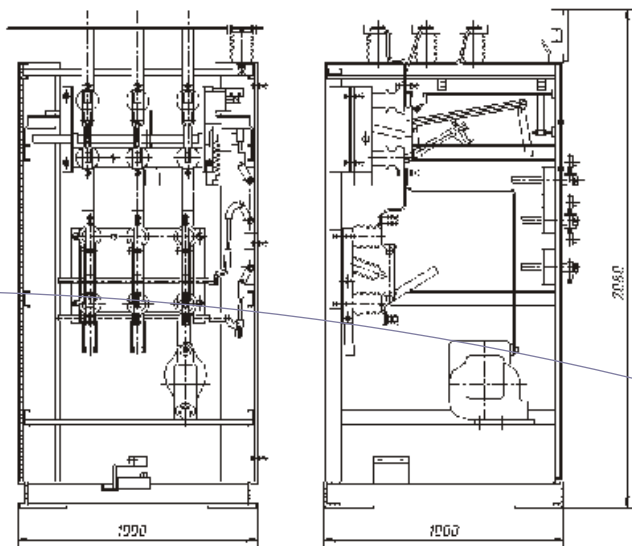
Камеры с разъединителями типа РВЗ: КСО-366М - 10-16з-630(400) УЗ
